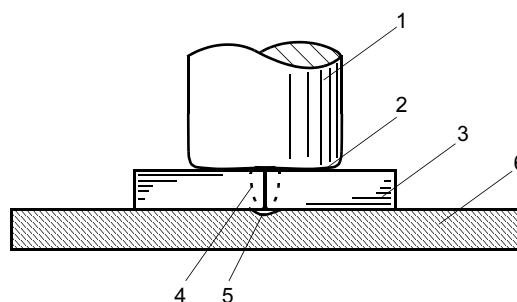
Сварка на подкладке с канавкой для принудительного формирования корня шва: 1 — пуансон; 2 — кромка пуансона; 3 — свариваемое изделие; 4 — рабочий стержень; 5 — канавка; 6 — подкладка
